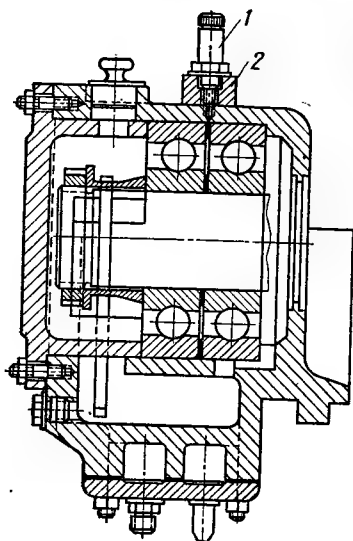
Схема установки термодатчика на корпусе подшипника:
